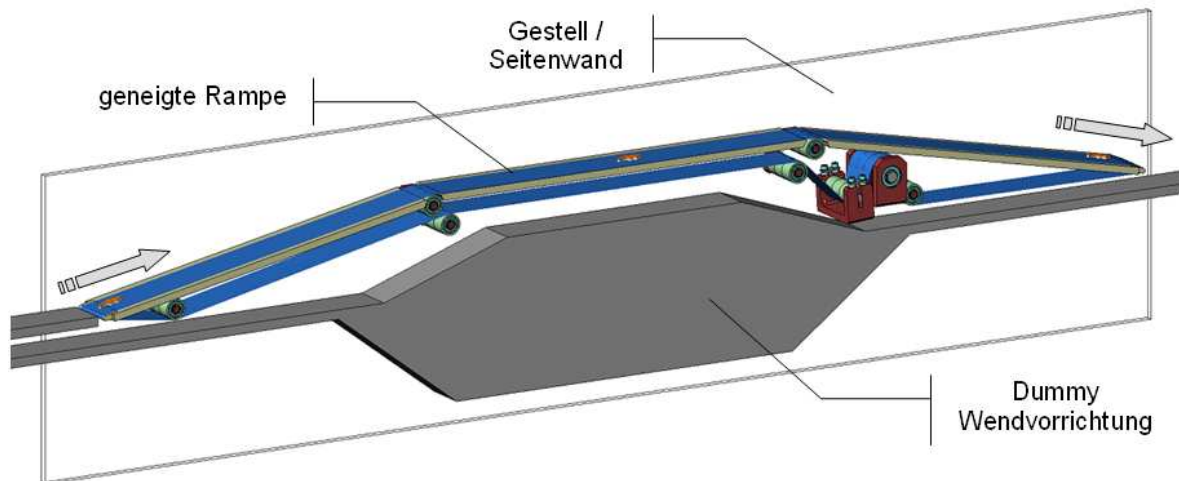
Gesamtansicht Konstruktion geneigte Rampe
